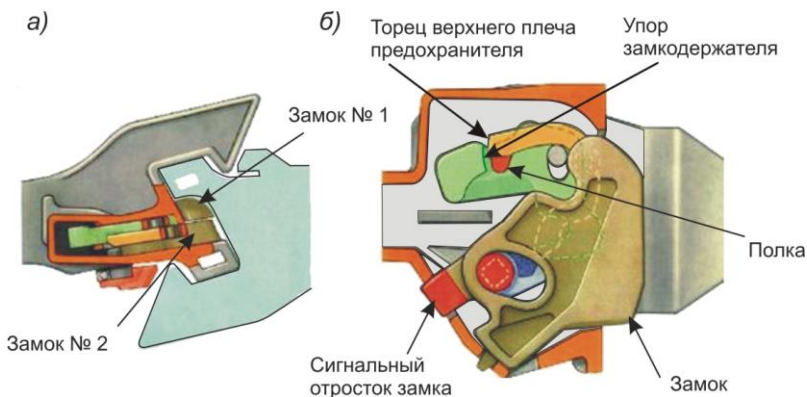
Положения деталей механизма сцепления автосцепок в конце сцепления:
